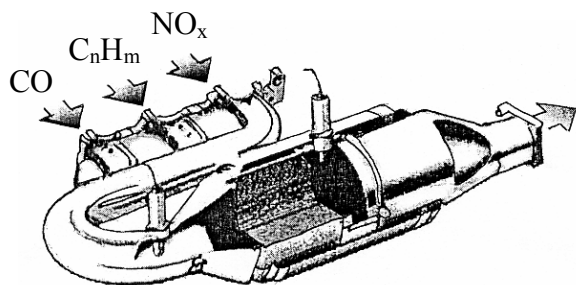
Конструктивна схема трикамерного каталітичного нейтралізатора ДВЗ
